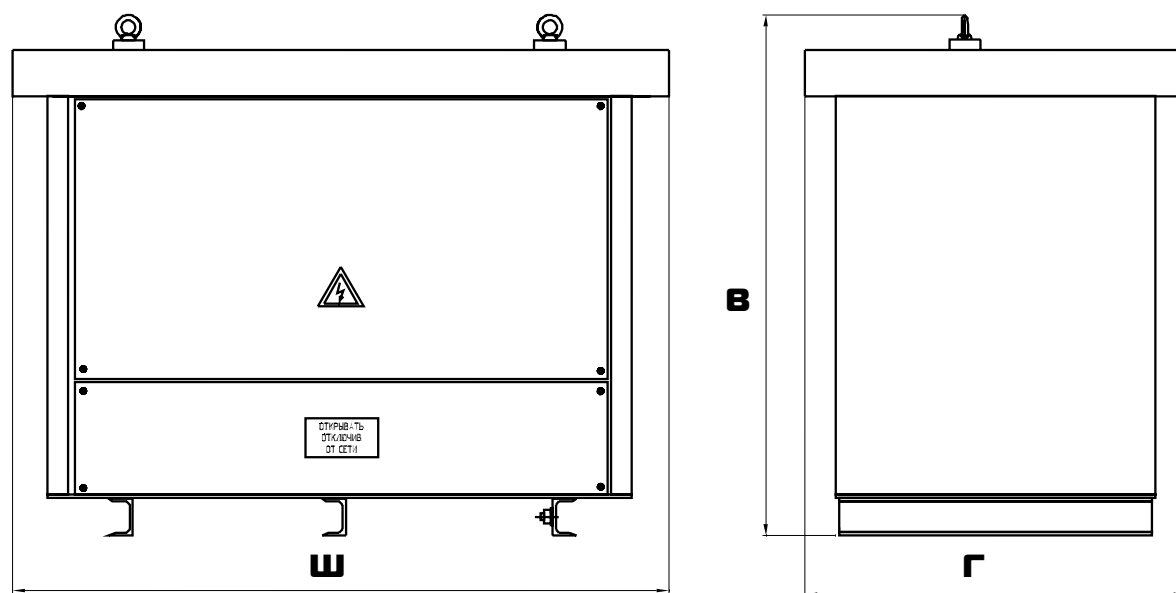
Габаритный чертеж СТС-5-М IP31 160 - 300 кВА
